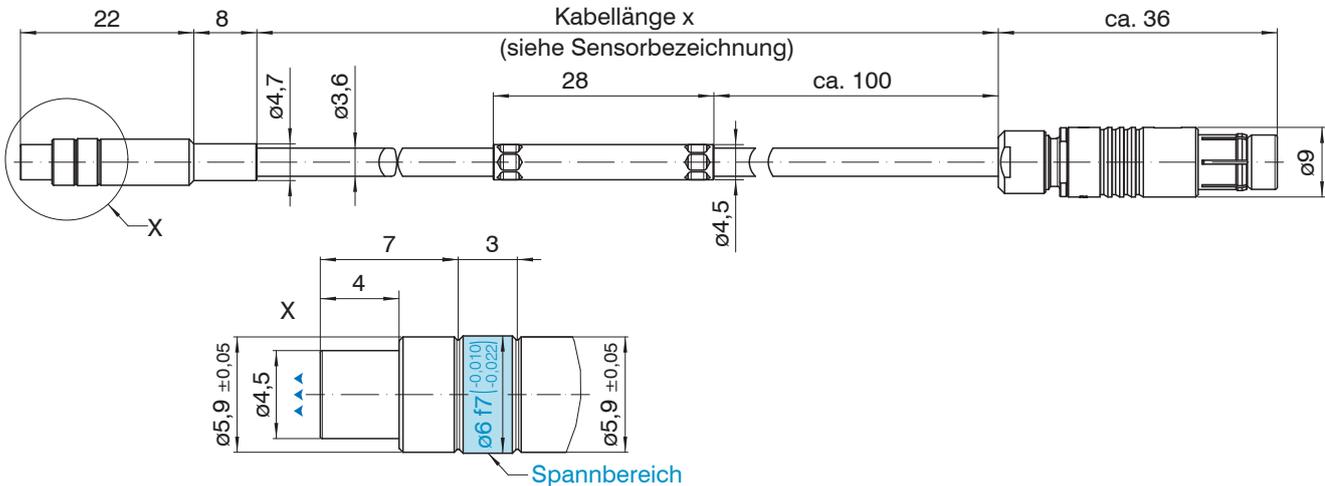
Maßzeichnung Sensoren ES-U1-T-CAX/mB0, Abmessung in mm
